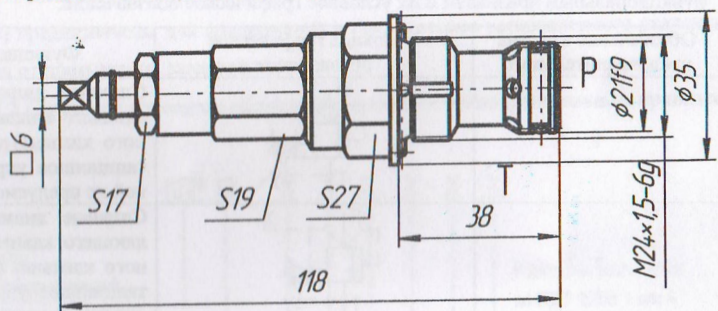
Габаритные и присоединительные размеры клапана предохранительного типа КПР 10/X BB1 – X1
